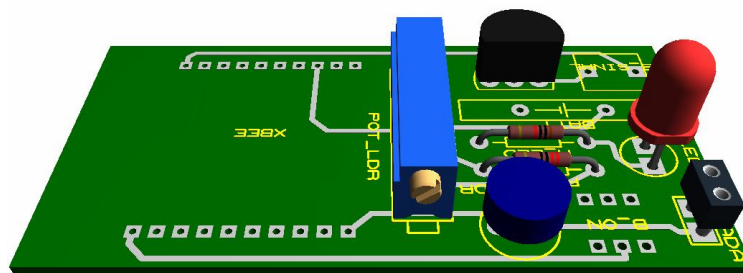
Desenho 3D da placa de Circuito Impresso dos Sensores Remotos
